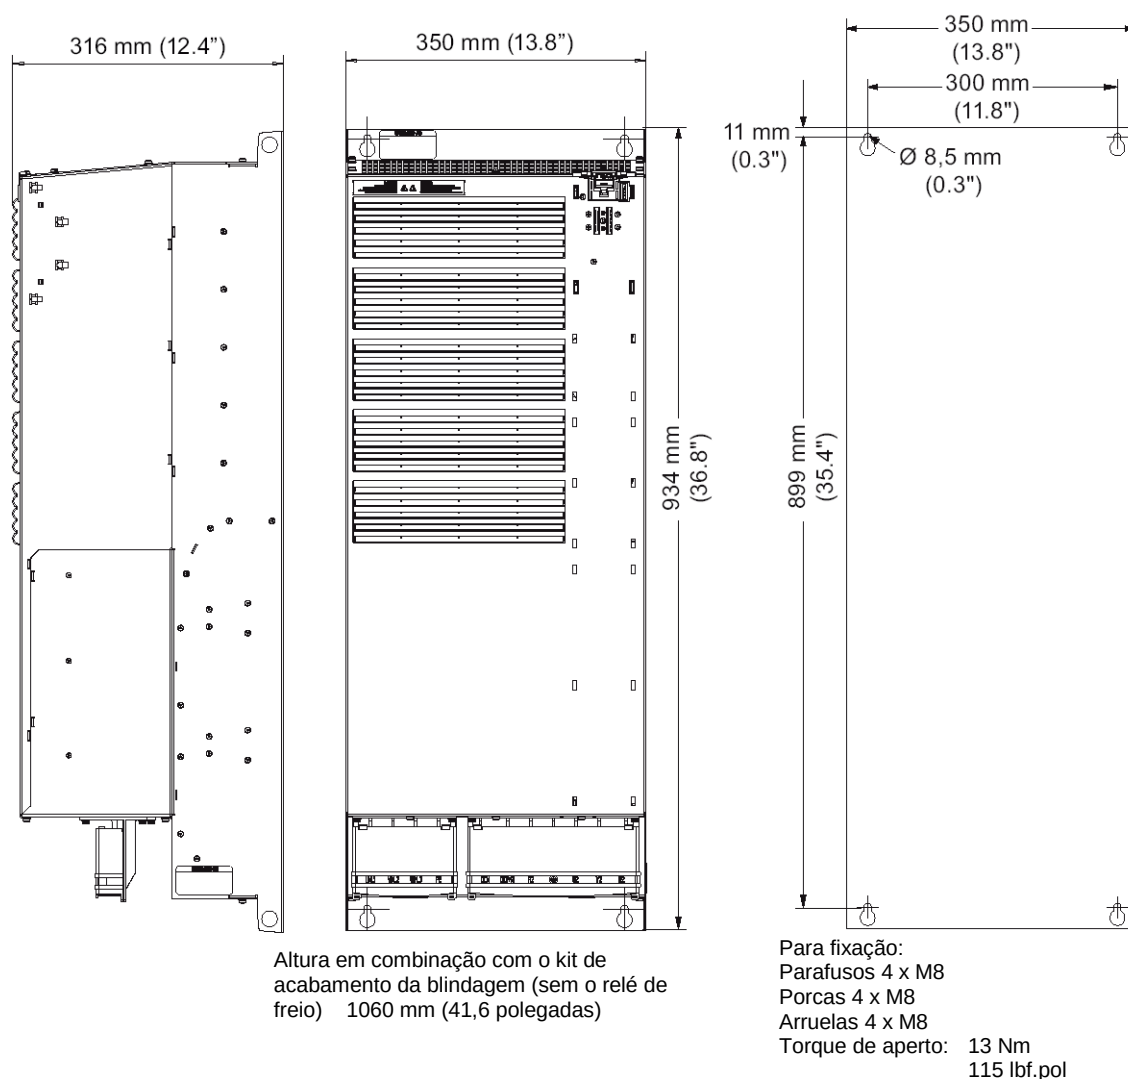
Dimensões e padrão de perfuração, FSF filtrado (HO 45 kW ... 75 kW)
